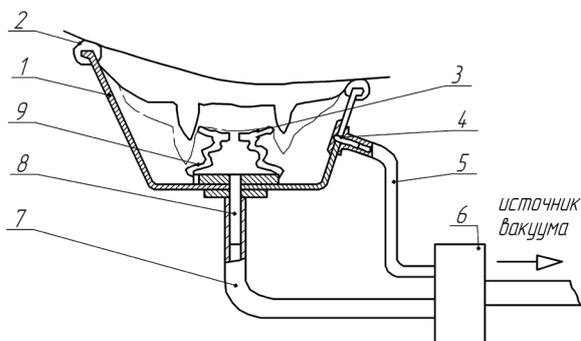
Схема устройства для массажа вымени животных однокамерного типа: 1 – кожный; 2 – уплотняющая прокладка; 3 – присосок; 4, 8 – патрубки; 5, 7 – шланги; 6 – пульсатор; 9 – пневмокамера
